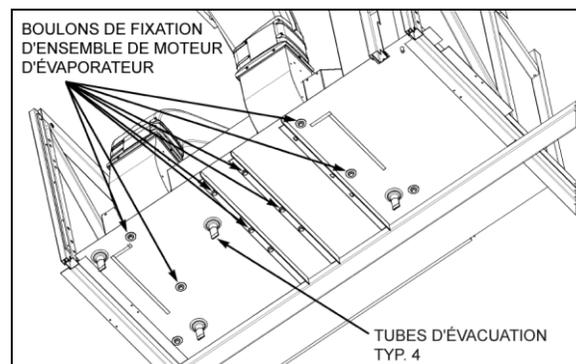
BOULONS DU MOTEUR DE L'ÉVAPORATEUR
